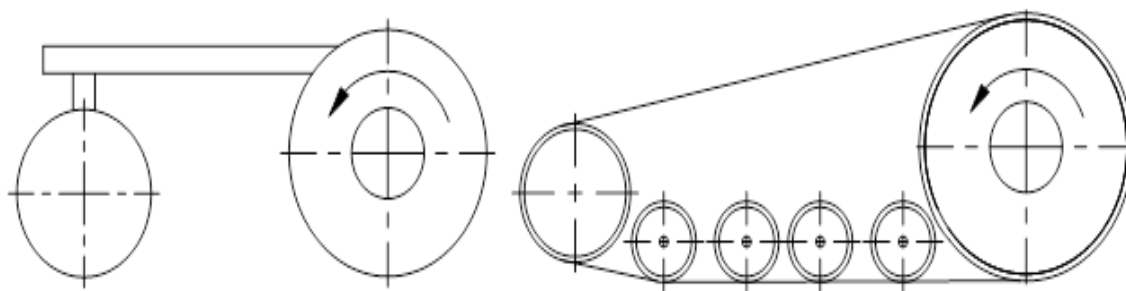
Схема сменного колесно-гусеничного движителя с увеличенными ведущими колесами
